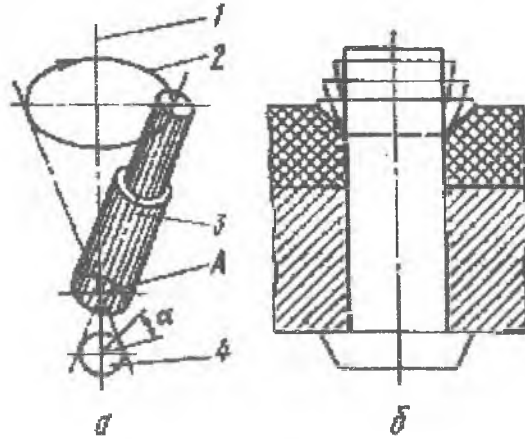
Схема процесса образования замыкающих головок при клепке давлением с раскаткой: а – движение инструмента; 1 – ось вращения шпинделя; 2 – траектория движения; 3 – ось инструмента; 4 – торец заклепки; б – этапы изменения формы головок
